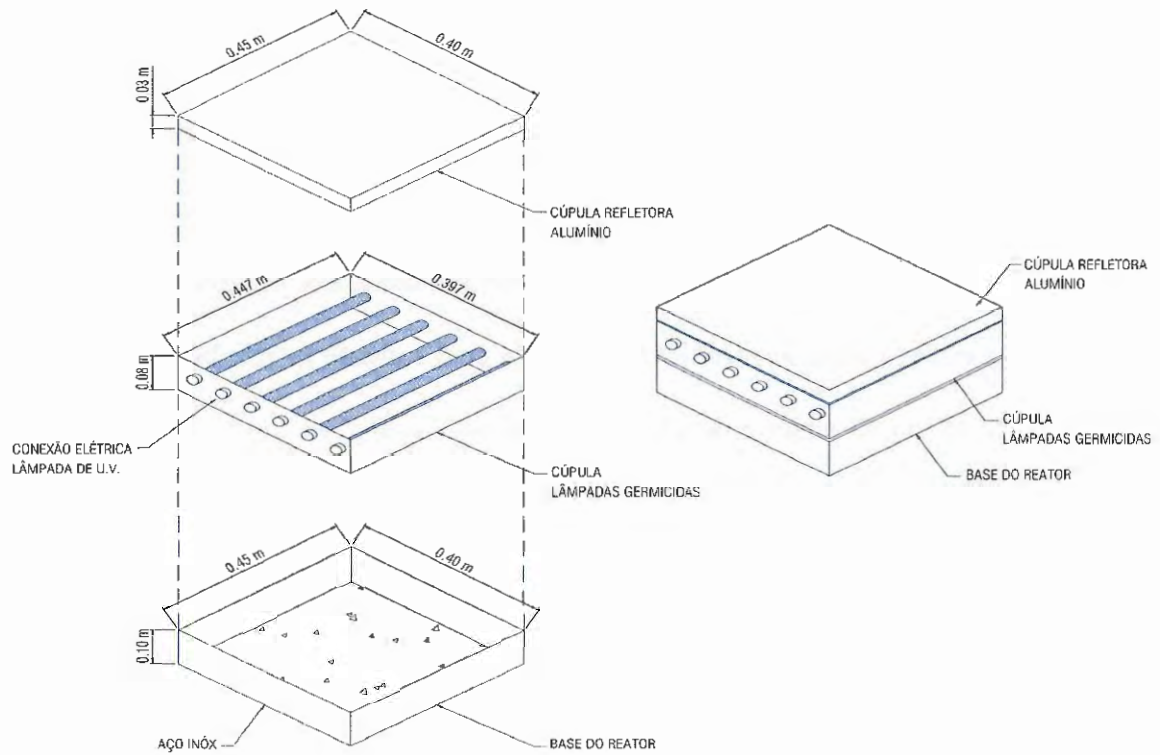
Detalhes das dimensões do reator de radiação UV.
